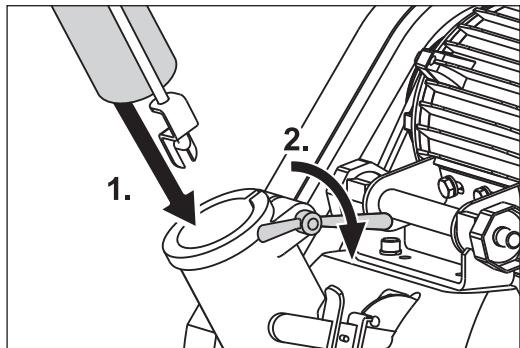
Das Führungsröhr in das Maschinengehäuse stecken (1.). Die Flügelmutter anziehen (2.).
